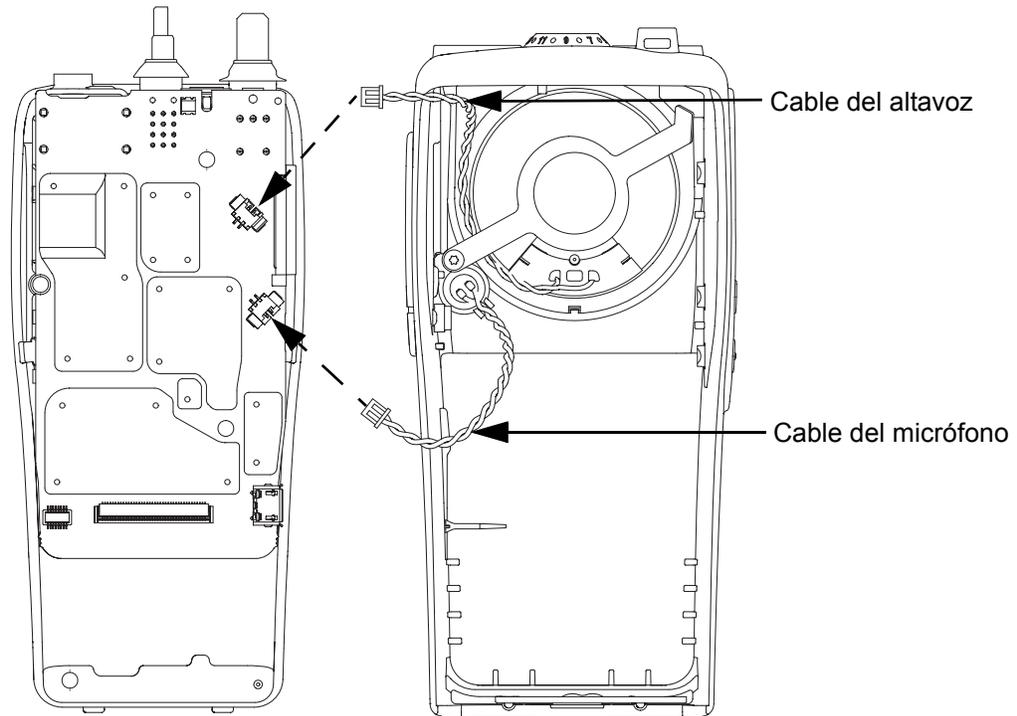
Rearmado del chasis y de la carcasa frontal
